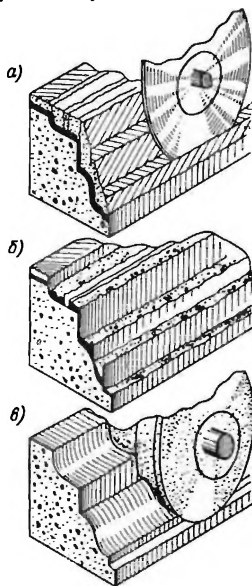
Порядок оформления профиля на универсальном фрезерно-окантовочном станке
